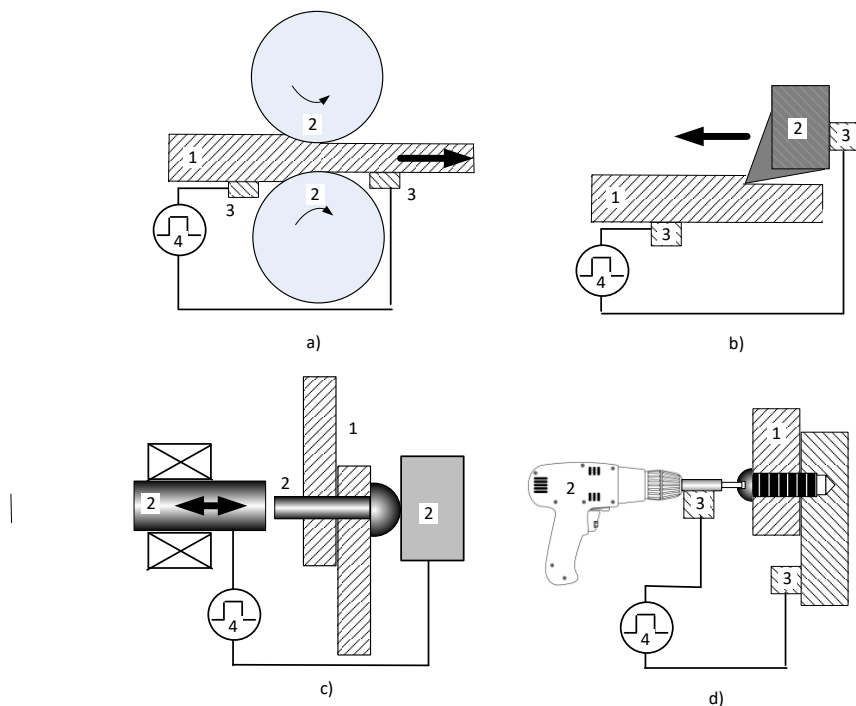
Применение ЭПЭ при обработке металлов давлением (прокатка – а, резка металла (проточка) – б, формировании неразборного соединения (клепка) – с, разборного соединения с использованием резьбового соединения – д.
